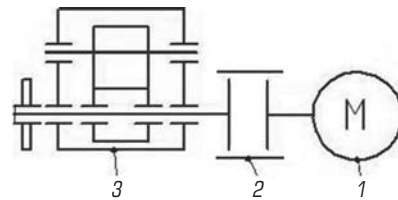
Кинематическая схема модернизированного привода щековой дробилки:
